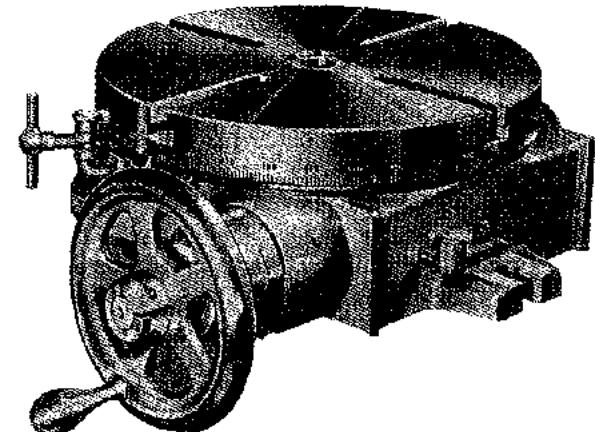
Plato giratorio con avance a mano (Cincinnati Milling Machine Co.)
